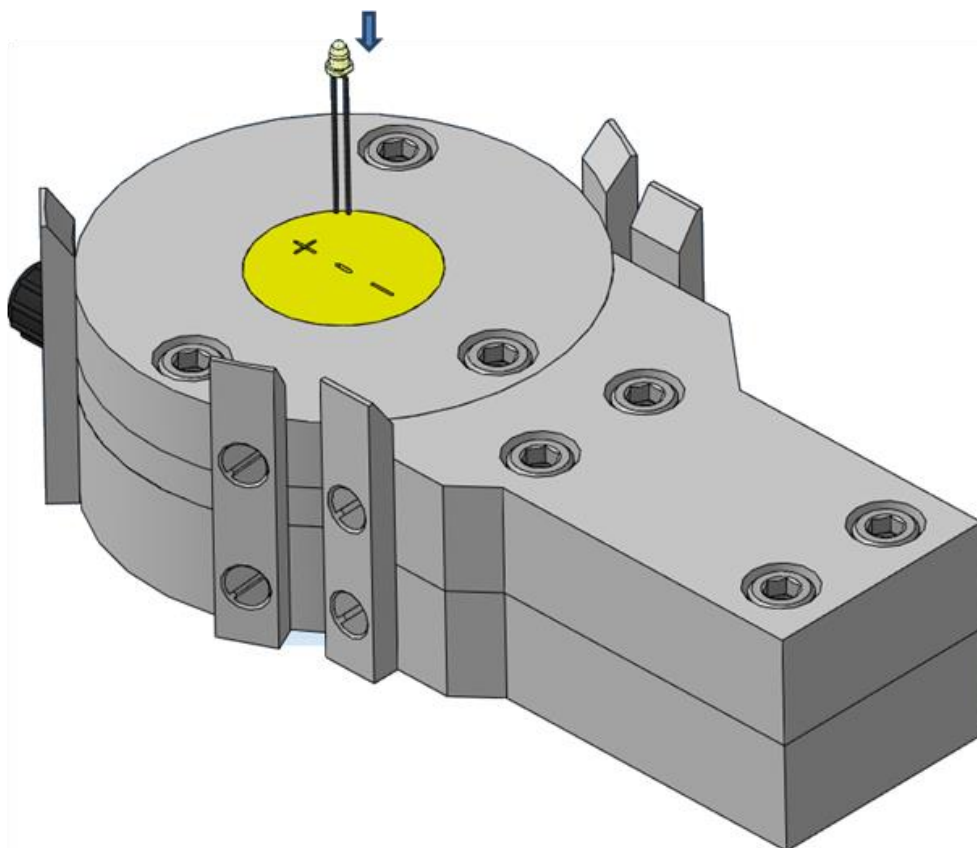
Посадочное место установки по исследованию светодиодов
